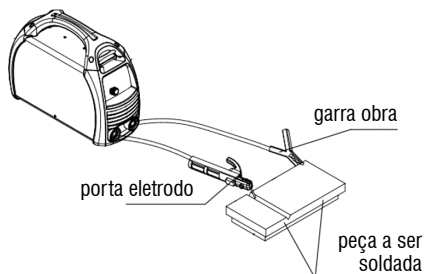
Montagem dos cabos de solda para soldagem de Eletrodo Revestido (MMA)
